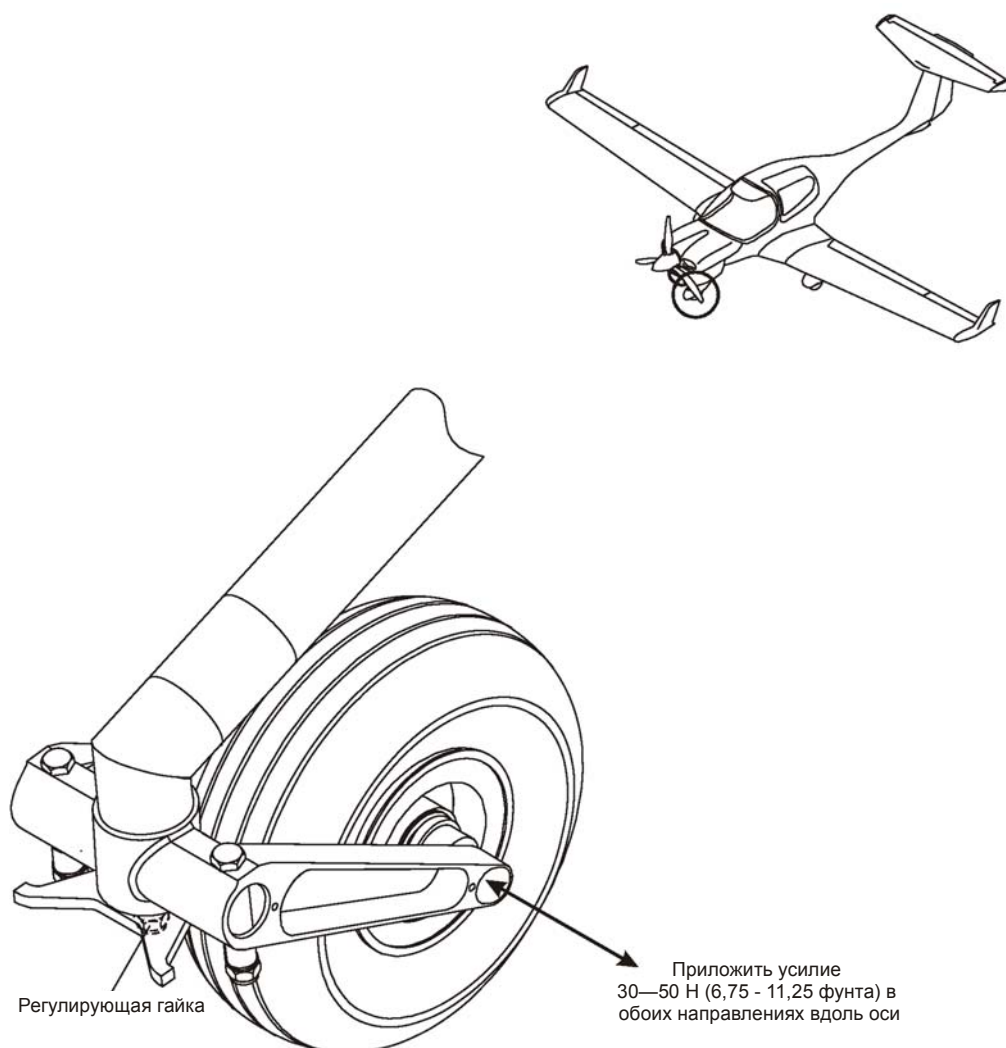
Регулировка усилия трения в шарнире вилки колеса носовой опоры
